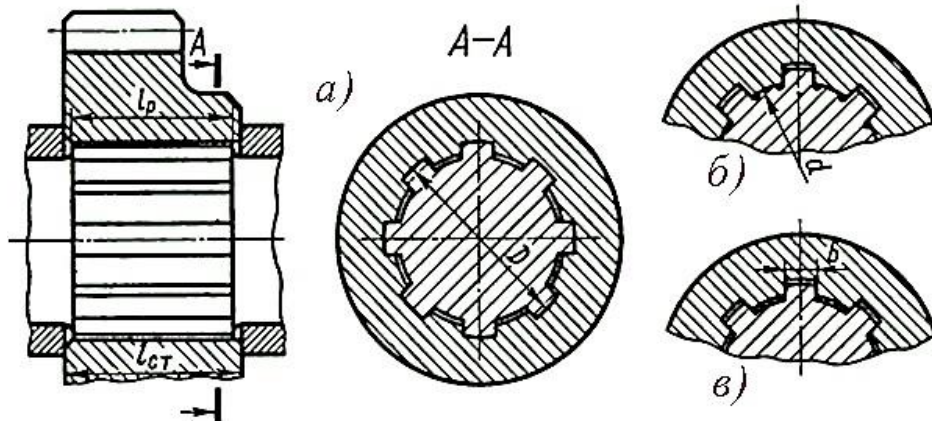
Шліцьові з'єднання з прямобічним профілем
